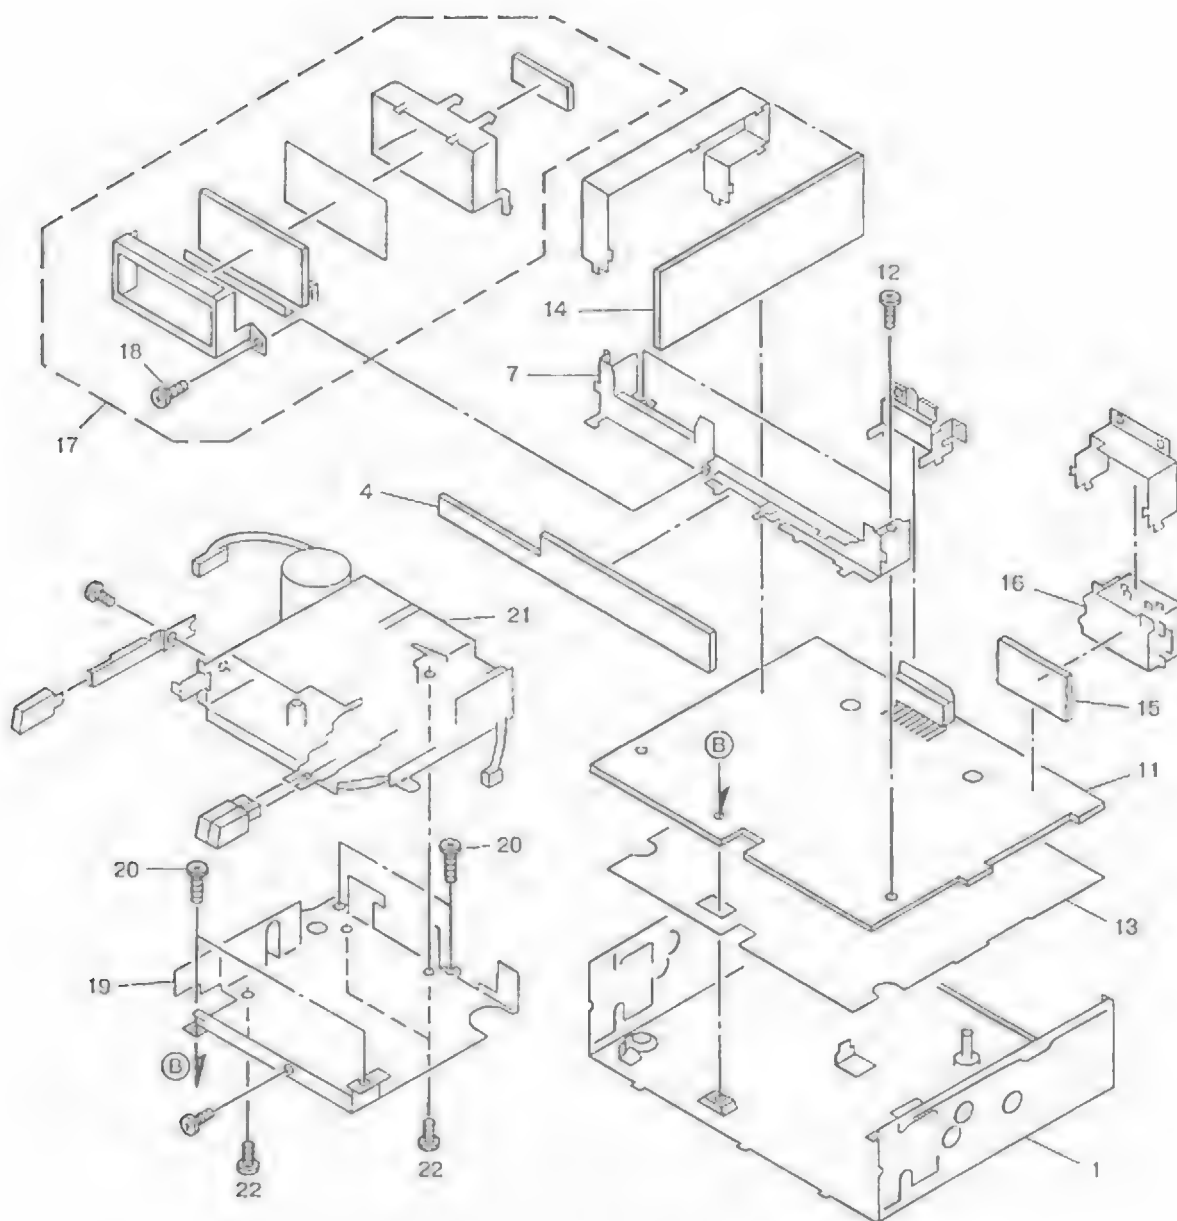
Схема разборки и сборки автомагнитол SONY XR-1950/1953
